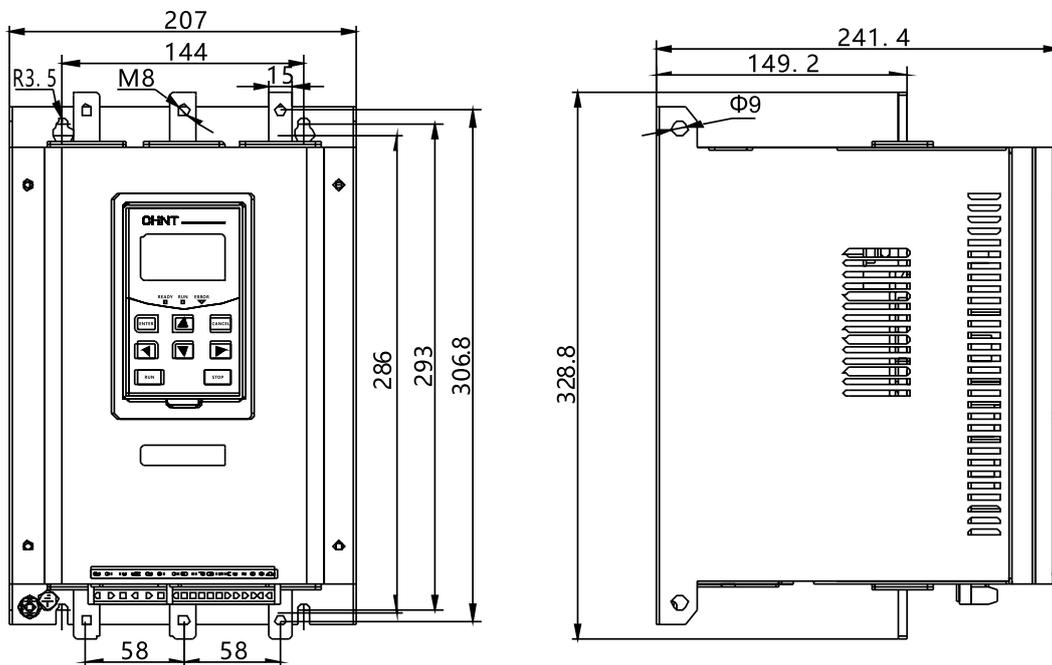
Общий компоновочный и установочный габаритный чертеж для устройств моделей NJR5-110/ZX3–NJR5-150/ZX3 и NJR5-110/ZX6–NJR5-150/ZX6
